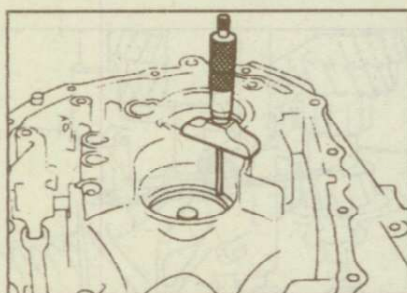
Измерение расстояния от привалочной поверхности картера сцепления до места установки наружного кольца подшипника
